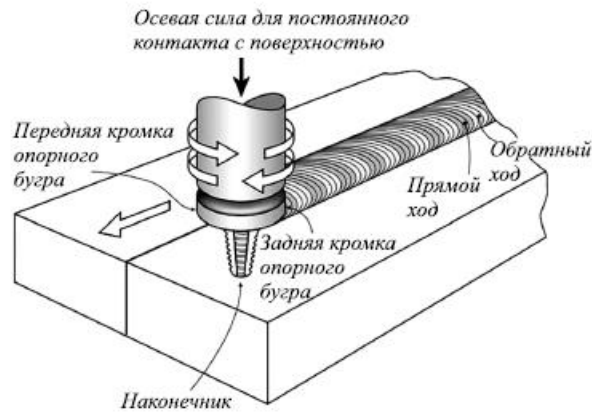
Схема процесса сварки трением с перемешиванием (СТП) [24].
